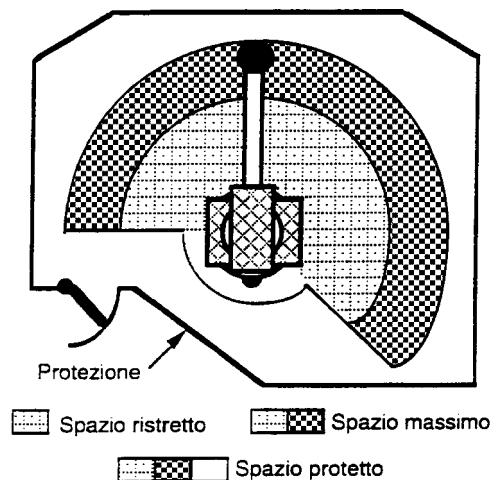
Esempio di spazio ristretto e spazio protetto
